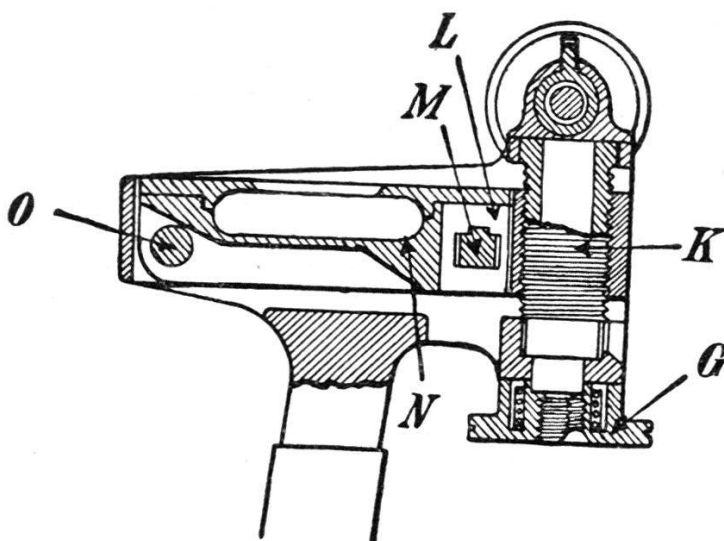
Hausse-niveau, coupe longitudinale sur le niveau.
